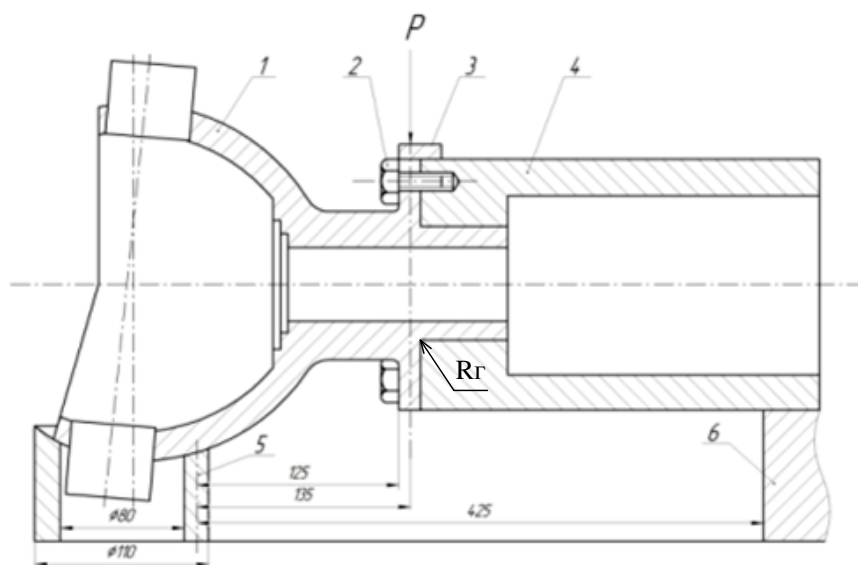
Схема нагружения шаровой опоры: 1 – шаровая опора; 2 – крепежные болты; 3 – накладка; 4 – труба; 5 – кольцевая опора; 6 – прямоугольная опора.
